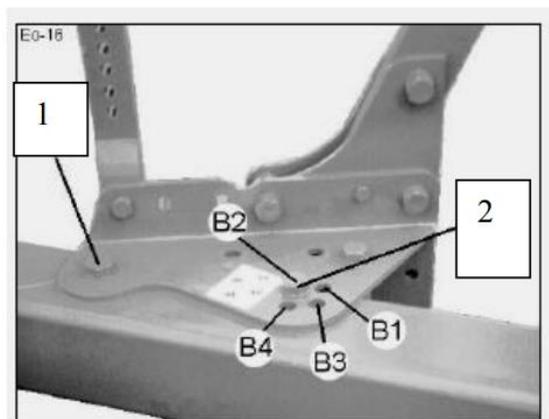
Установка ширины захвата каждого корпуса по схеме перестановки (позиции В1-В4): 1 – центральный винт; 2 – регулировочный винт
